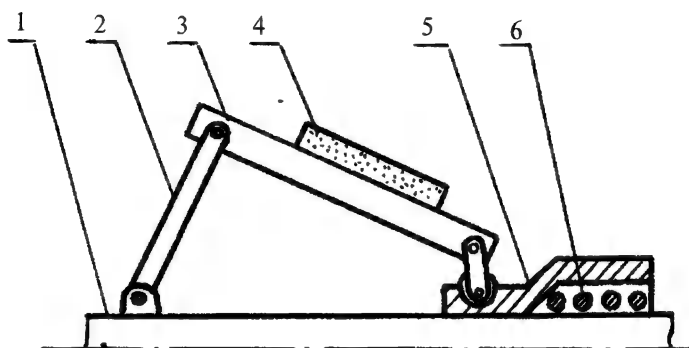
Хонинговальная головка для обработки конических отверстий: 1 - тяга, 2 - рычаг, 3 - колодка, 4 - абразивный брусок, 5 - плунжер, 6 - пружина.
